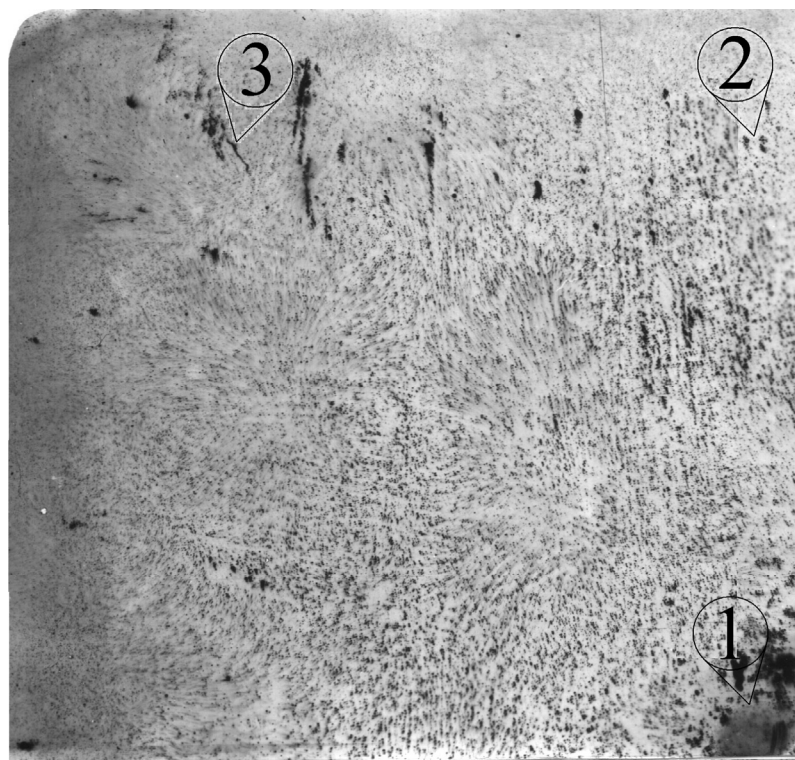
Сернистый отпечаток поперечного сечения (четвертая часть) непрерывнолитой исходной заготовки из стали марки СтЗсп ( $\times 1,3$ ):
